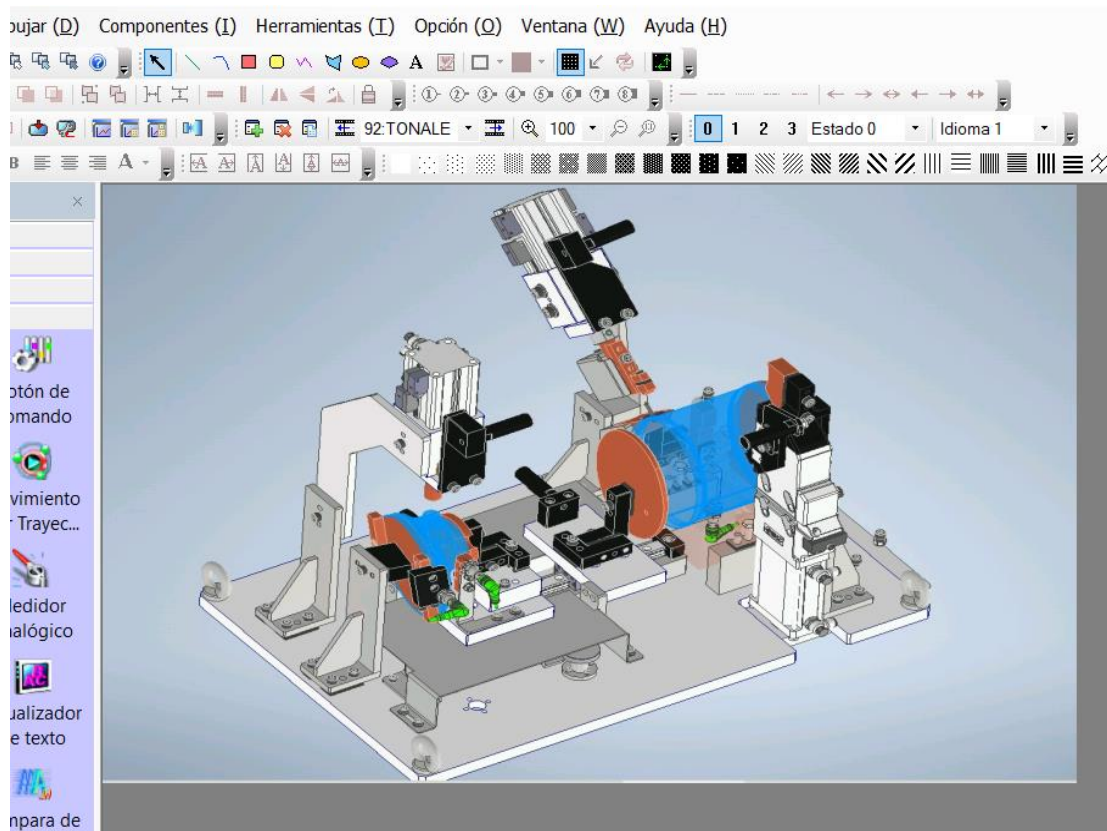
Imagen 1 fondo de pantalla. Fuente. elaboración propia
